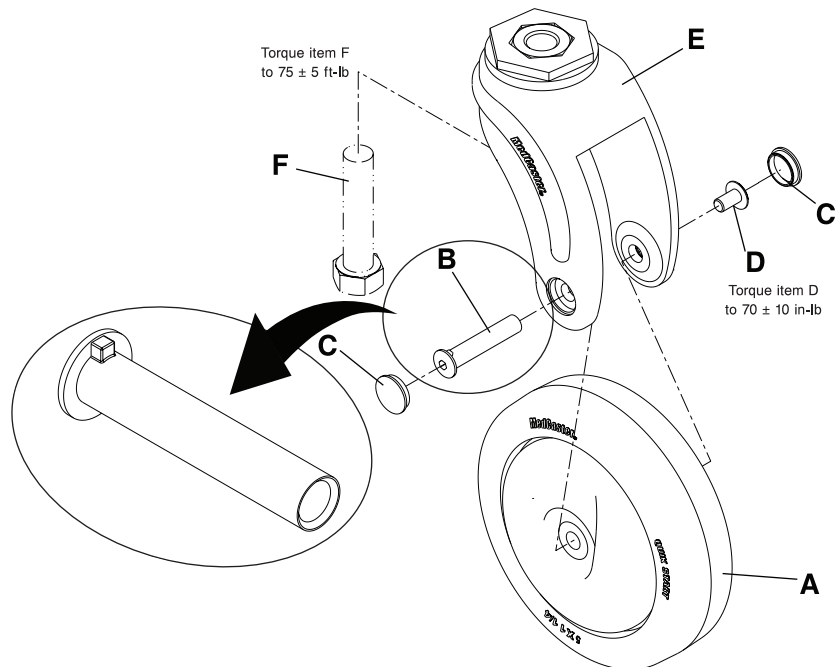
Remplacement d'un ensemble de roulette avant
